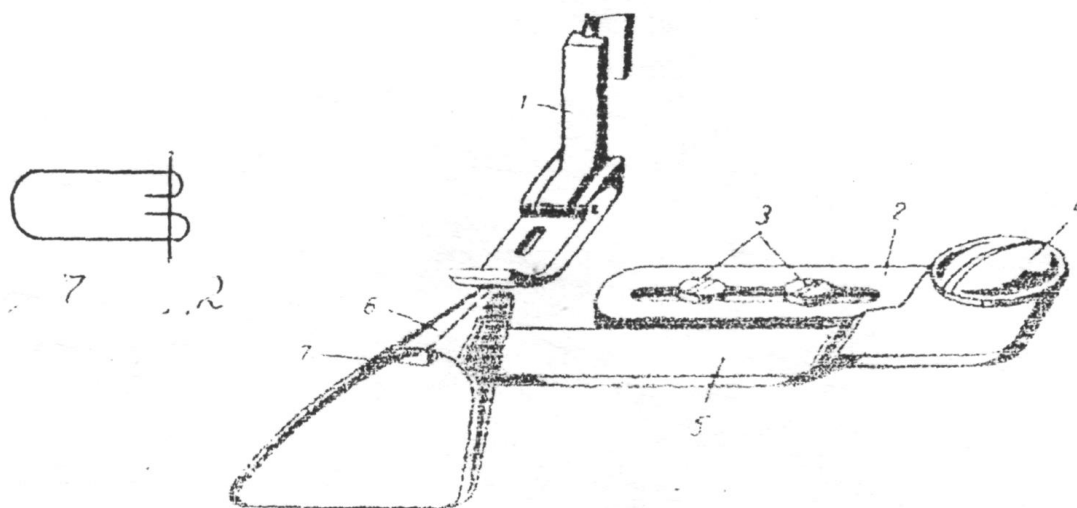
Приспособление для изготовления петель внутренних карманов и вешалок
